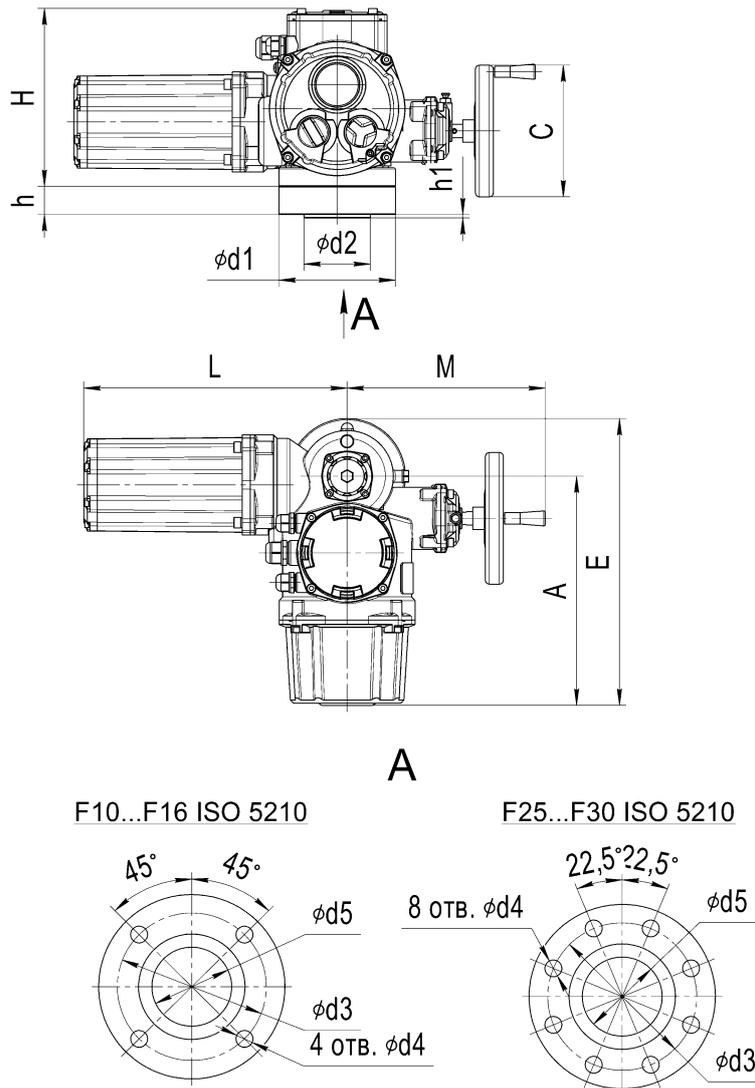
Габаритные и присоединительные размеры механизмов МЭМ15.3
